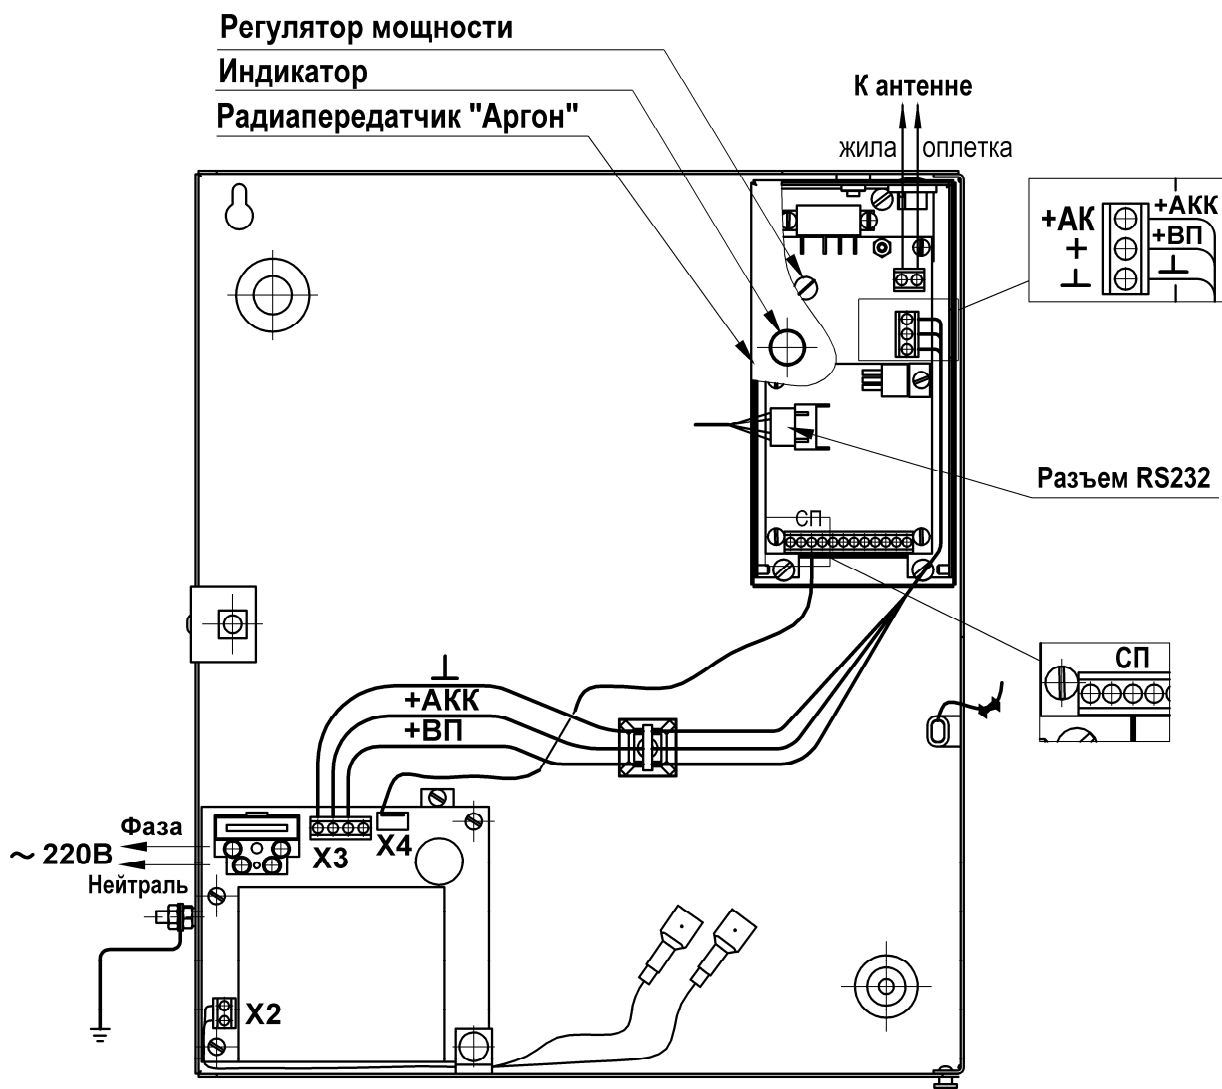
Вид блока передающего со снятой крышкой
